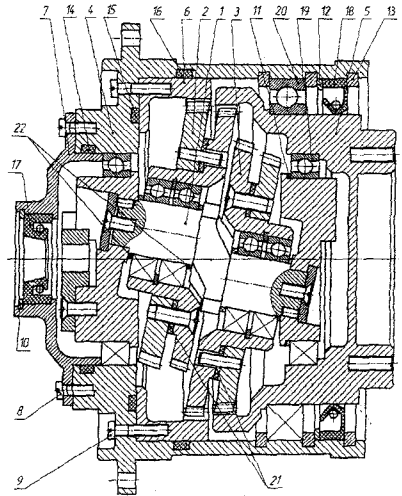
Конструкция планетарного редуктора с наклонными сателлитами
